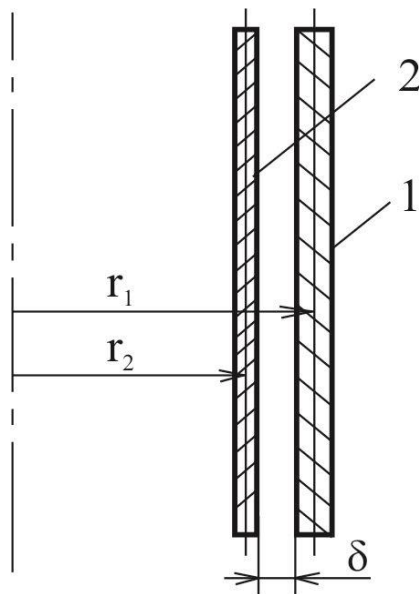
Схема розташування деталей, що зварюються: 1 – зовнішня деталь; 2 – внутрішня деталь.
